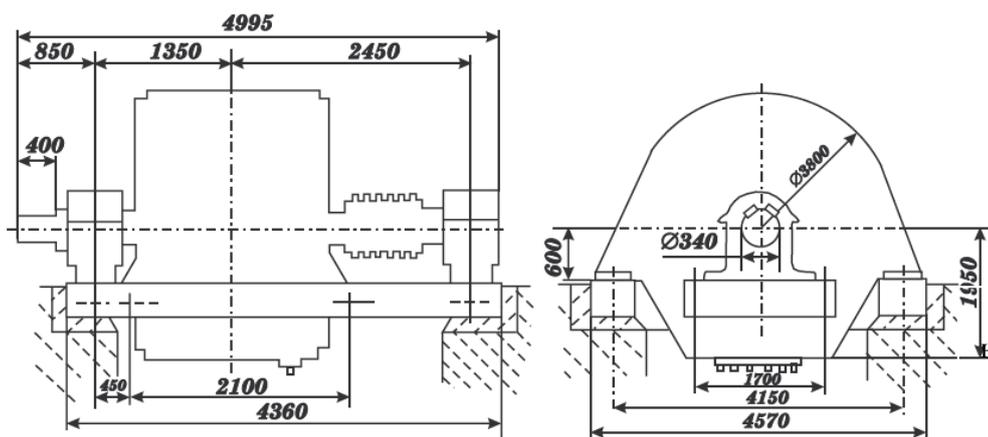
Габаритные, установочные, присоединительные размеры двигателя
